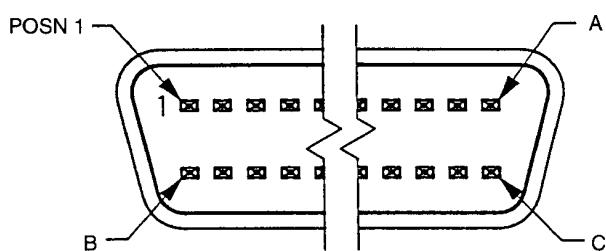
Face d'accouplement d'un connecteur avec contacts mâles
